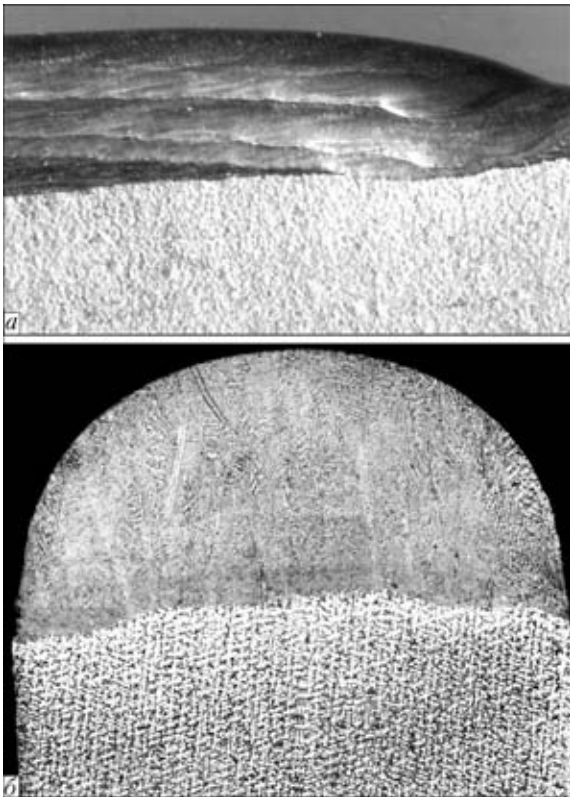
Внешний вид (а, X5) и макрошлиф (б, X25) трехслойной наплавки на торец образца (направление наплавки [013], плоскость наплавки (100), плоскость шлифа (031))
